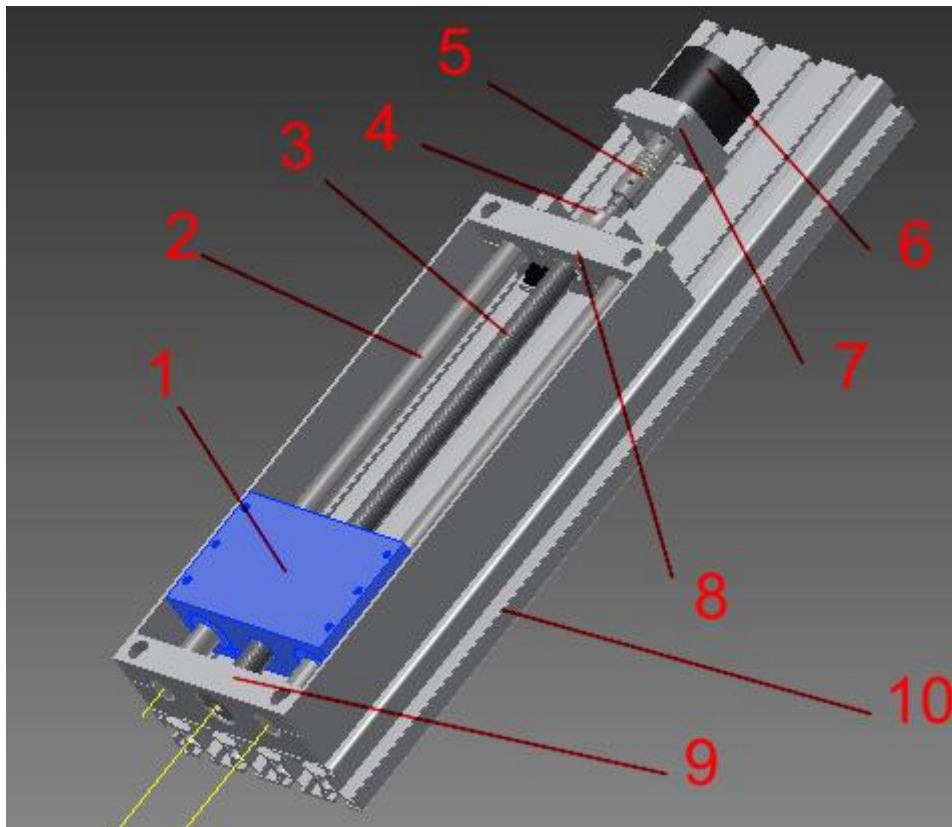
Координата по осям ОХ та ОУ, де: 1 – рухома каретка; 2 – циліндрична направляюча; 3 вал d12x5 (Табл.1.5), 4 – підшипниковий вузол (Табл.1.6), 5- муфта, :6-кроковий двигун;
